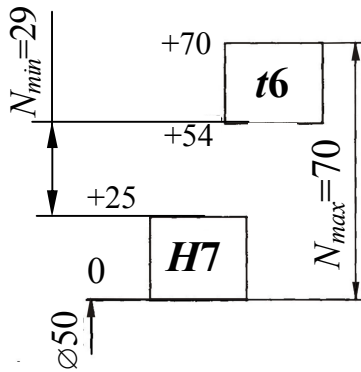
Схема полів допусків для посадки зубчастого колеса на вал
